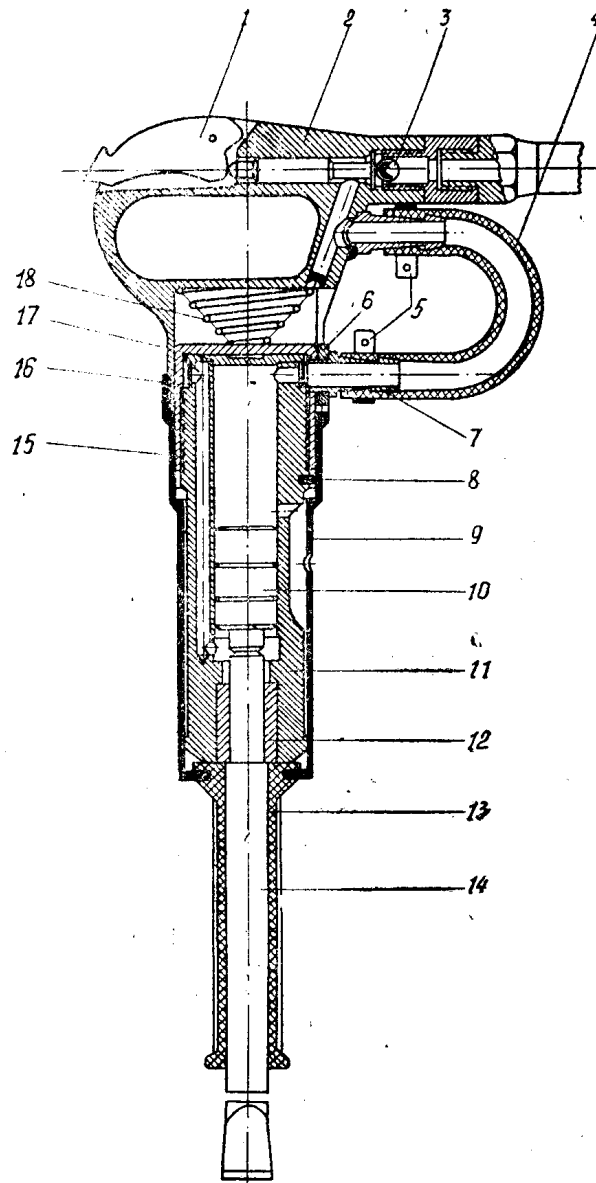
Устройство пневматического молотка БСЗ-135В. 1 — курок; 2 — рукоятка; 3 — шарик; 4 — шланг; 5 — хомут; 6 — фиксатор; 7 — штуцер; 8 — стопор; 9 — ложный ствол; 10 — ударник; 11 — ствол; 12 — букса; 13 — муфта резиновая; 14 — рабочий инструмент; 15 — промежуточное звено; 16 — клапан; 17 — крышка клапана; 18 — пружина конусная
